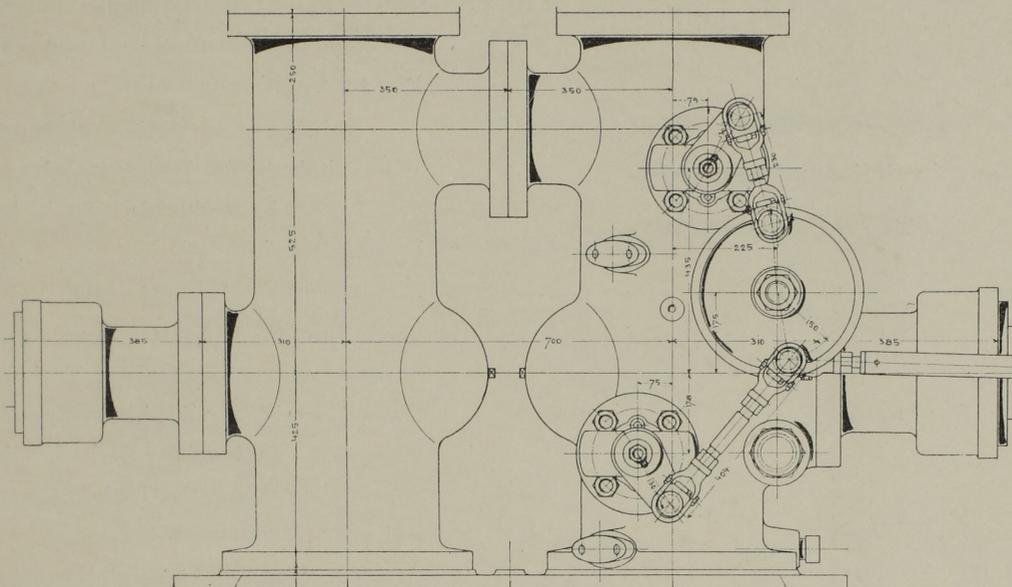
Seitenansicht und Pumpensteuerung. Massst. 1:5.
